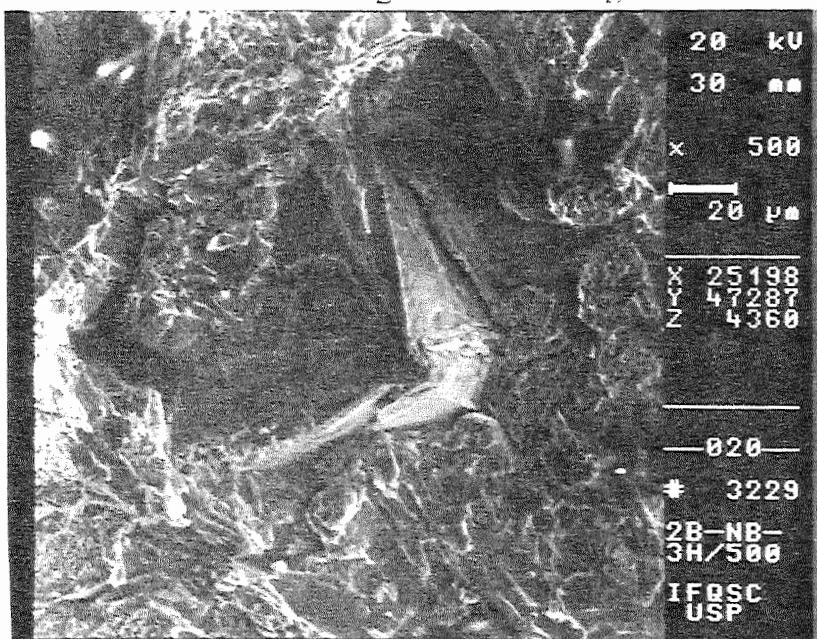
Superfície de fratura. Material aquecido 3 h a 1020°C, resfriado ao ar e reaquecido 3 h a 500°C. Regiões de fratura frágil por clivagem, de carbonetos e de fratura fibrosa referente à matriz
